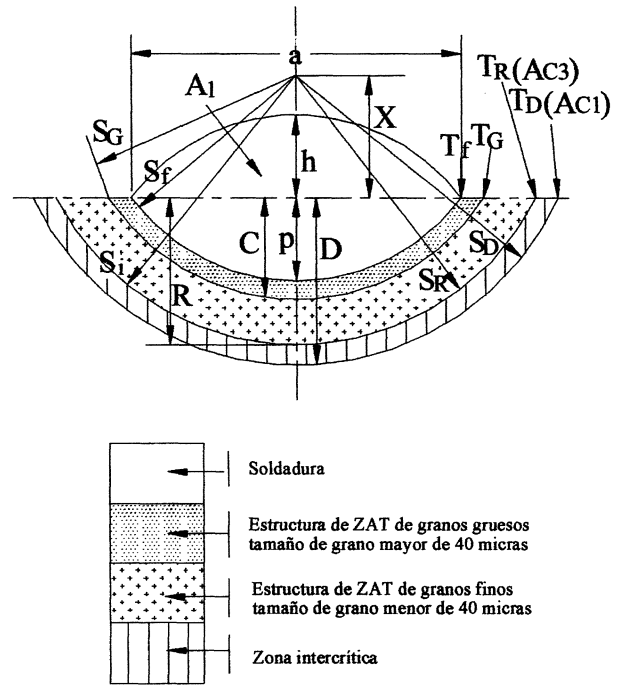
Esquema idealizado de un cordón de soldadura.
